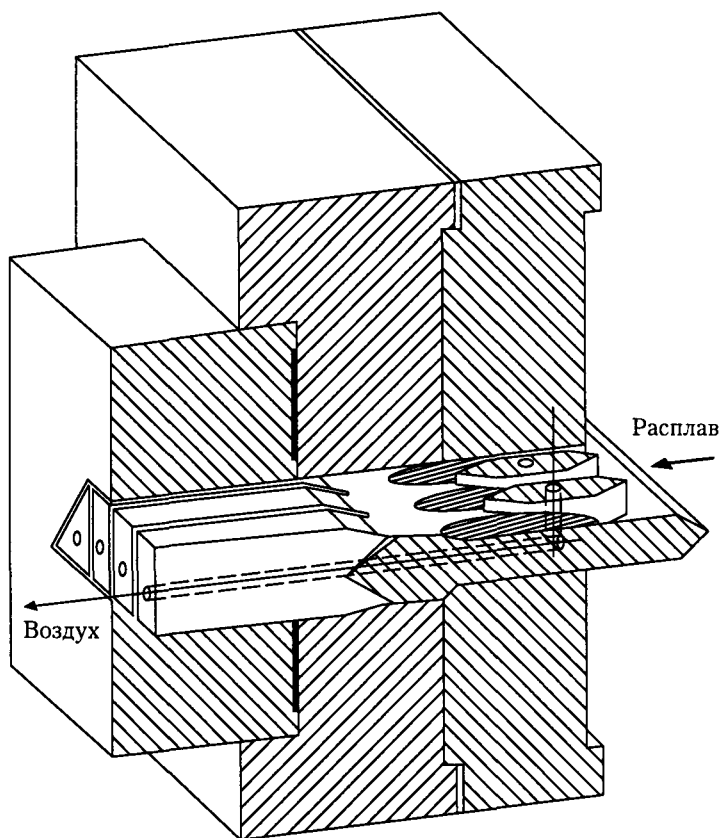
Схема блендовой головки с дорнодержателем [5]
